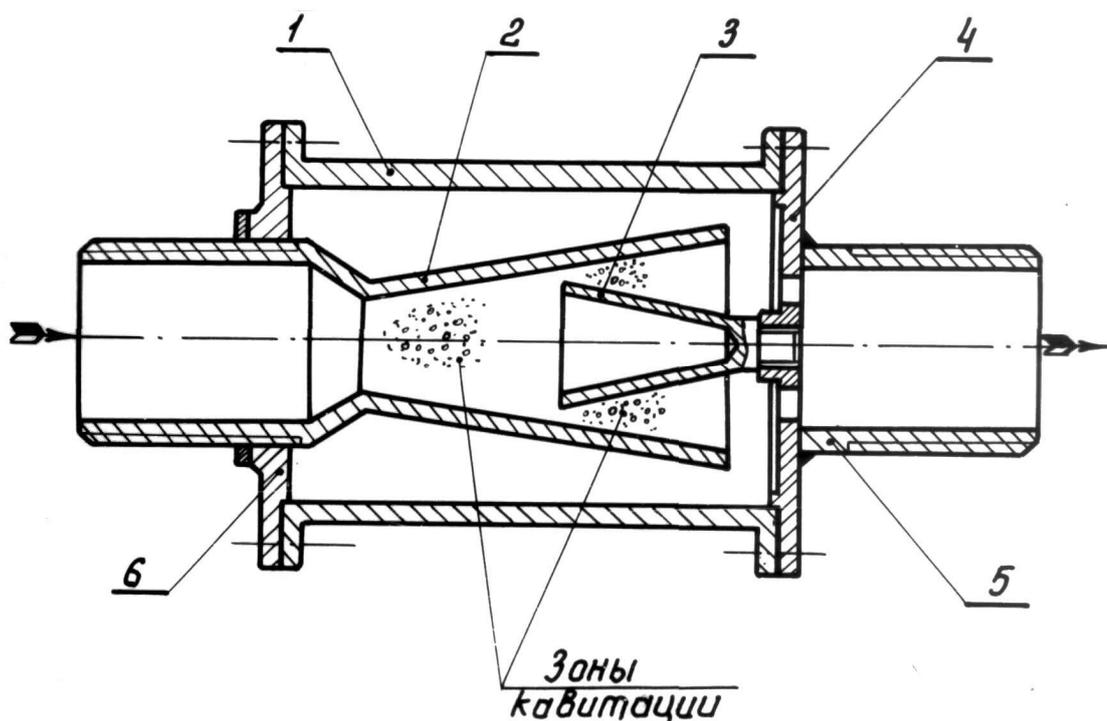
Ультразвуковой диспергатор: 1 – корпус; 2 – сопло; 3 – резонатор; 4 – крышка; 5 – выпускной патрубок; 6 – крышка
